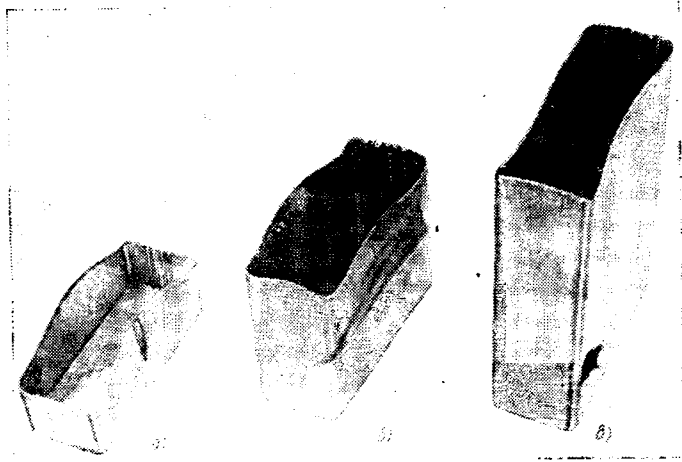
Характерные дефекты при выдавливании коробчатых деталей: а — разрыв стенки; б — складка; в — отрыв дна
